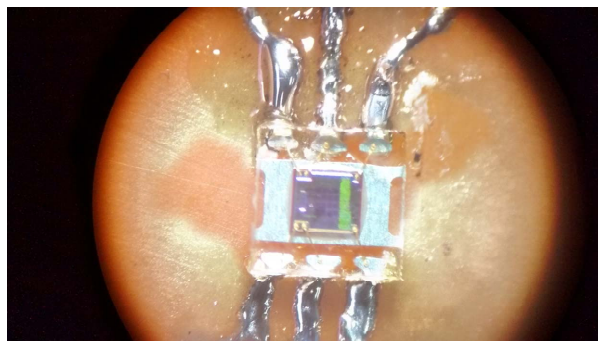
Imagen de sensor OPT3001 soldado sobre circuito impreso visualizado mediante lupa estereoscópica Moticam 30x de zoom.
